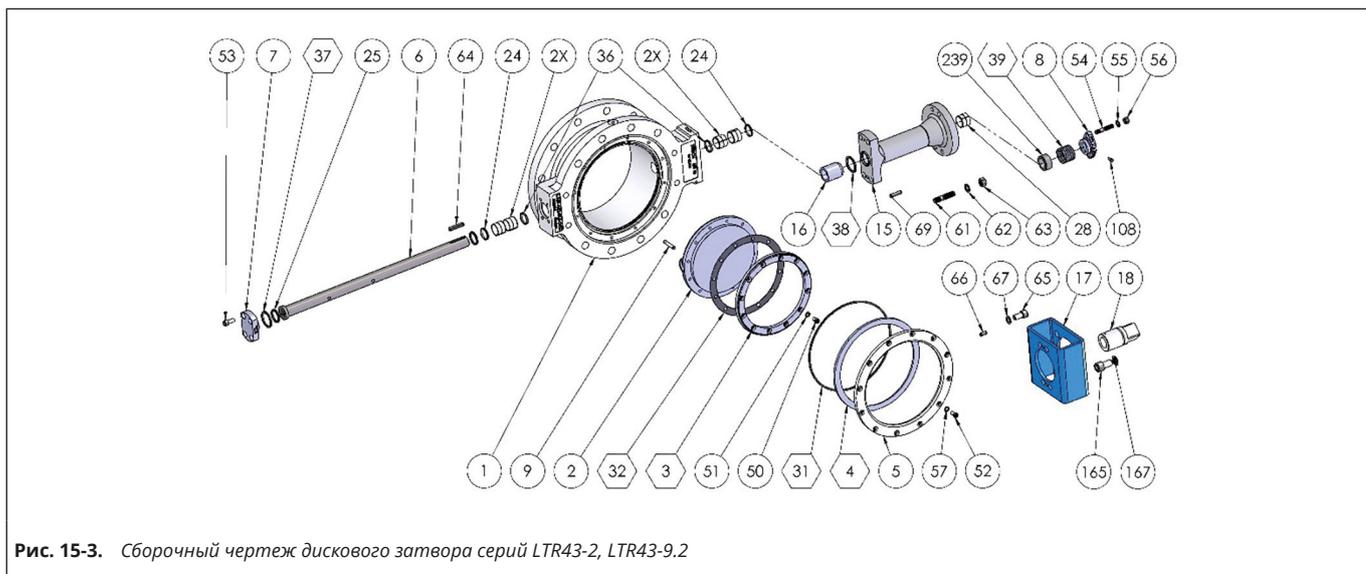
Сборочный чертеж дискового затвора серий LTR43-2, LTR43-9.2
